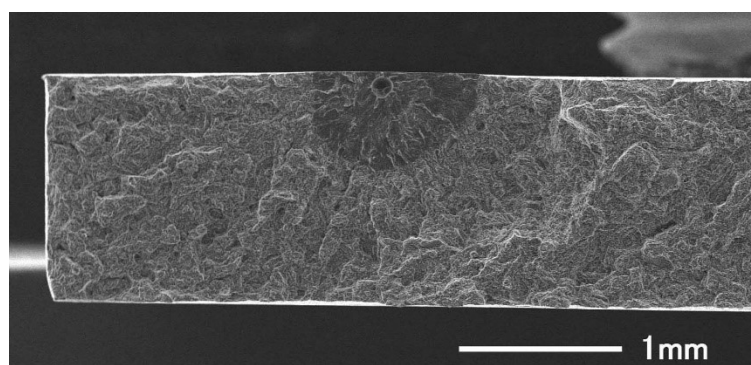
板厚 1.5 mm 溶接継手材における疲労試験後の破面
